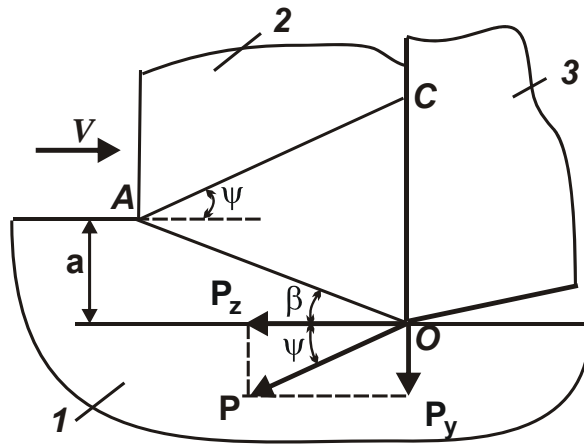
Расчетная схема параметров стружкообразования при резании: 1 – обрабатываемый материал; 2 – образующаяся стружка; 3 – режущий инструмент
